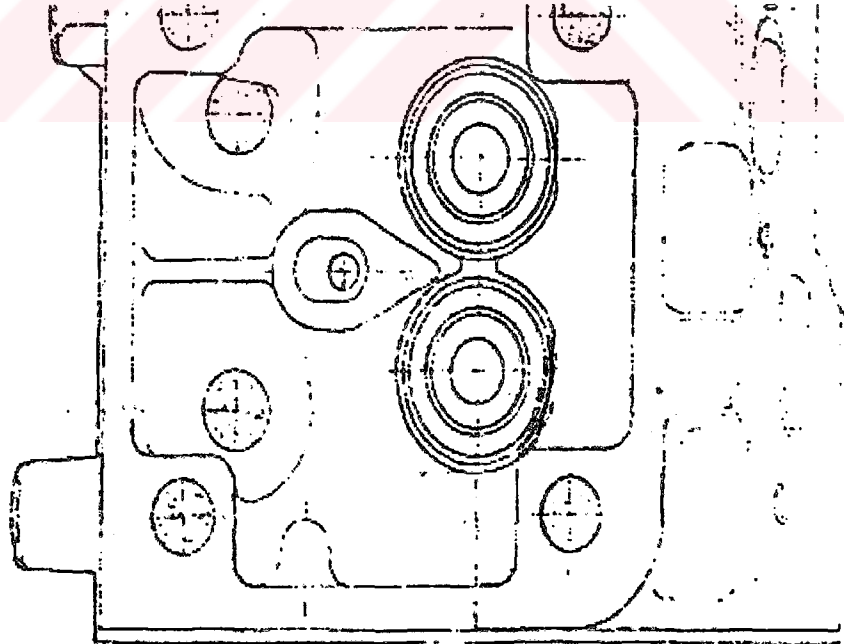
'de görüldüğü gibi motor kafasının alt kısmından 5 mm'lik eksen mesafesinden motor kafası ile gaz iletim borularının bağlantısı için 18 mm derinlikte M6x1 kılavuz çekilmiştir.
